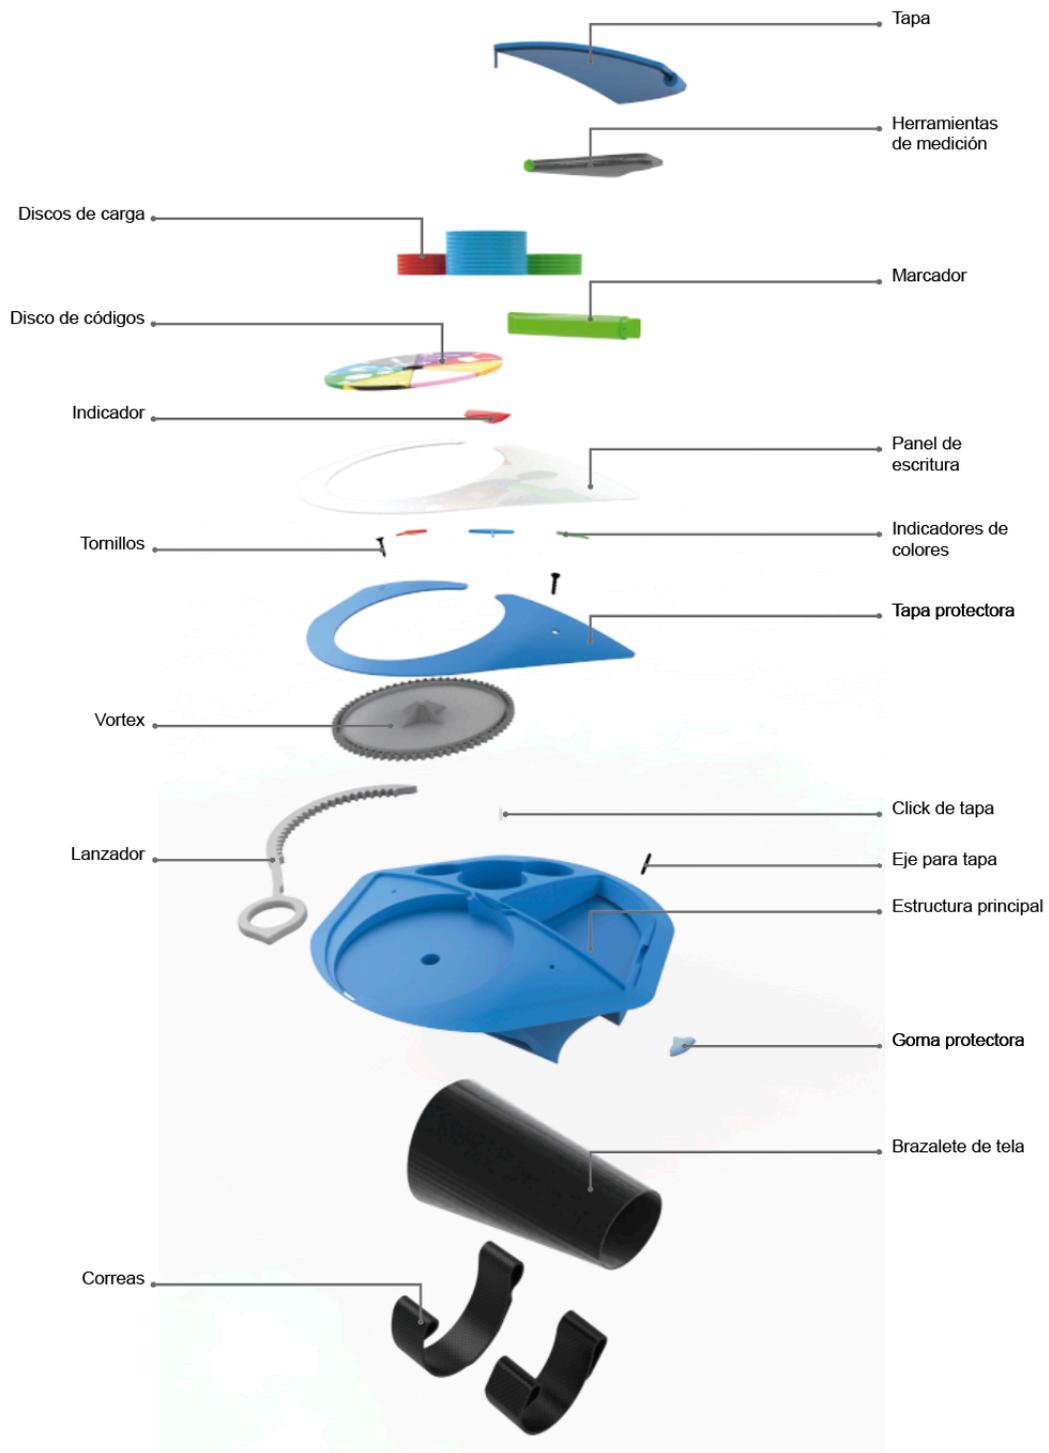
Explosión y despiece del Octobrazalete. Fuente: elaboración propia.
